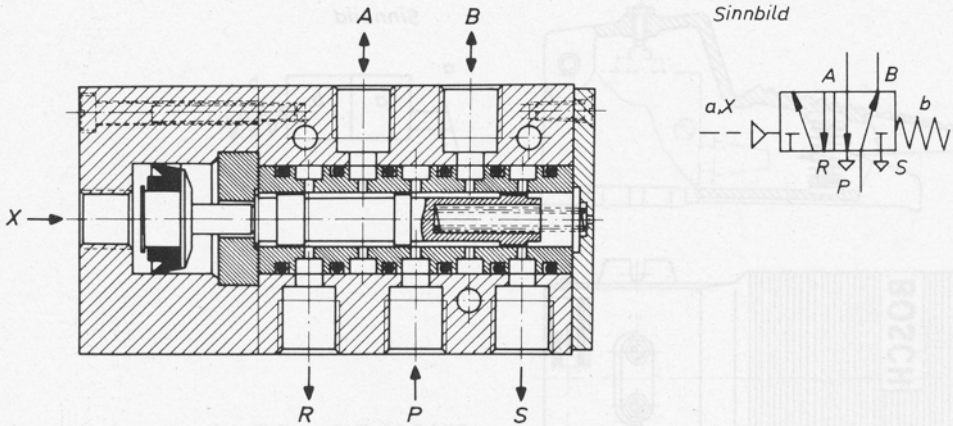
Pneumatisch betätigtes Ventil mit Rückstellfeder (Herion)
